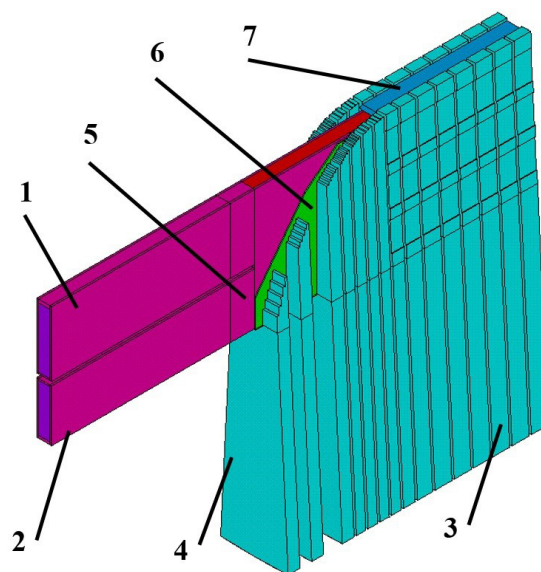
Модель статора турбогенератора в лобовой части, выходе обмотки из паза и в пазовой части в пакете ANSYS: 1 – верхний стержень обмотки статора; 2 – нижний стержень обмотки статора; 3 – основные пакеты сердечника статора; 4 – торцевые пакеты сердечника статора; 5 – поверхность, закрытая замазкой, расположенной между соседними стержнями в месте выхода обмотки статора из паза; 6 – изоляционная коробка; 7 – клин пазовый
